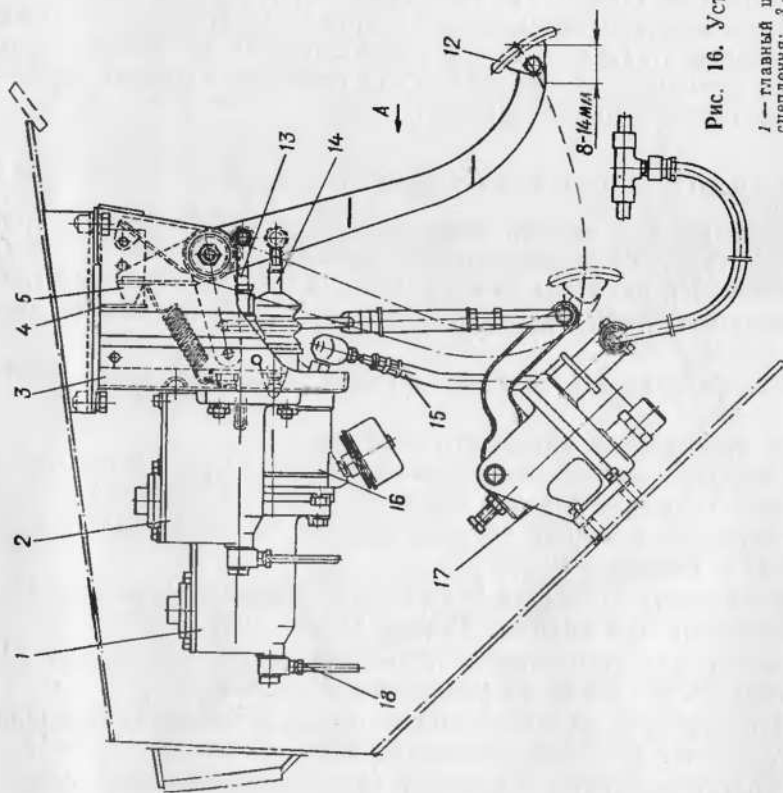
Установка главного цилиндра гидравлического привода тормозов:
